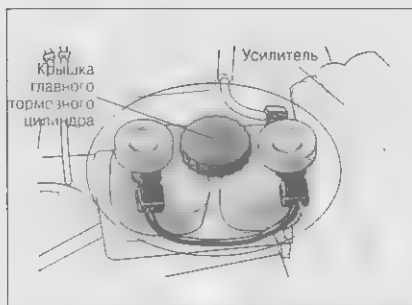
Пластиковая крышка главного тормозного цилиндра
